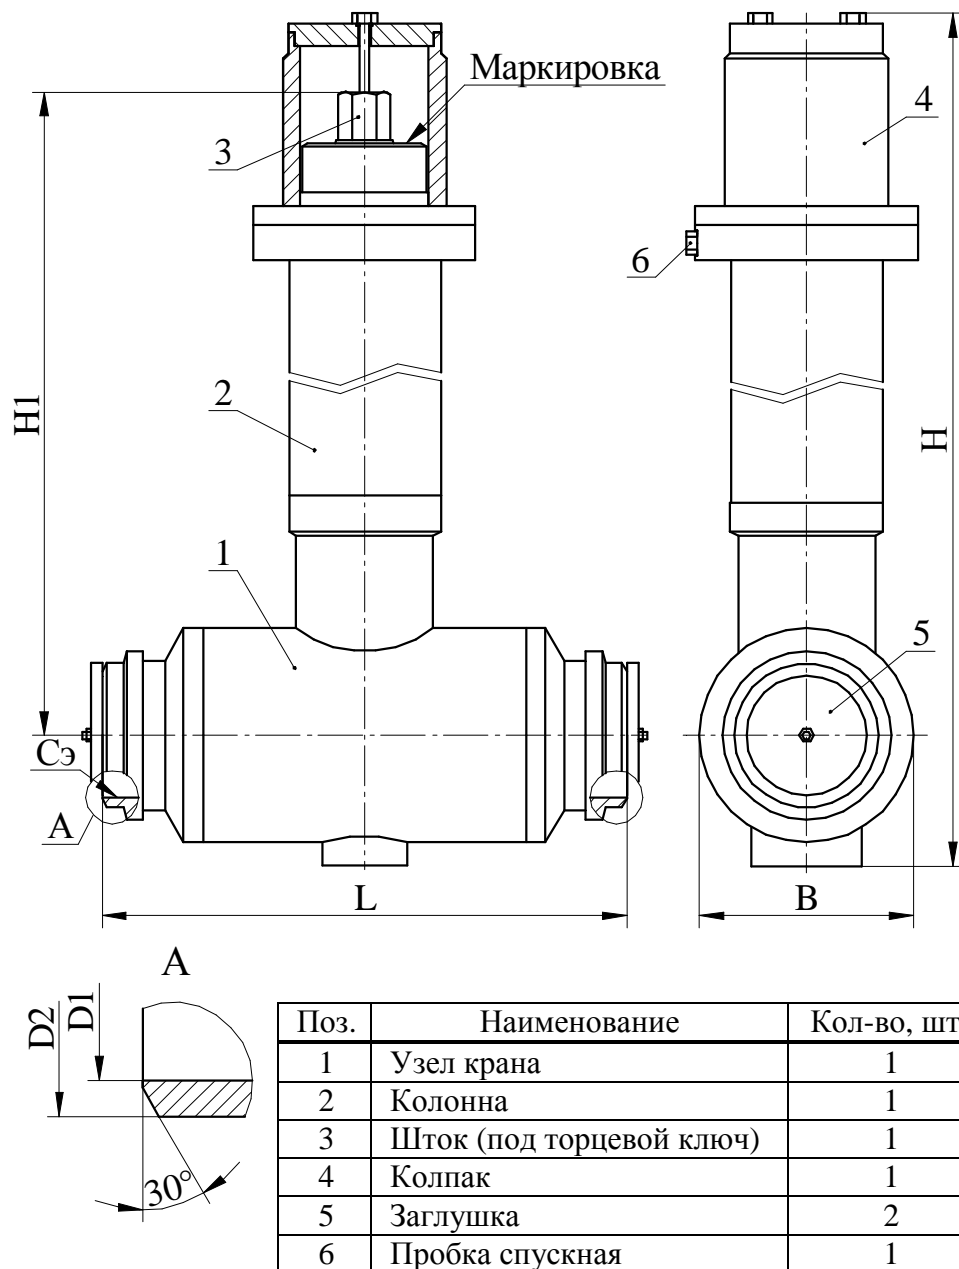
Кран шаровой подземной установки (под ковер) с ручным управлением (под торцевой ключ) с концами под приварку
